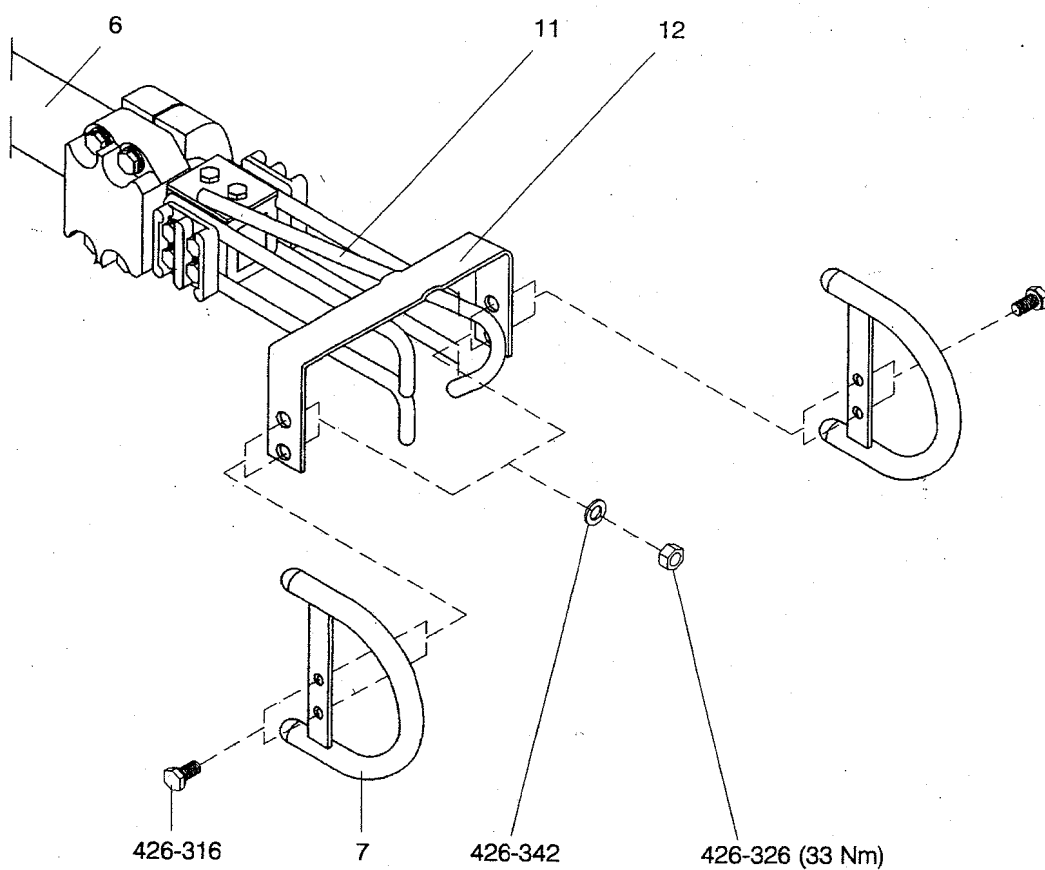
Установка разъединителя. Установка устройств защиты от короны (7) на пальцевой стороне (только для номинального напряжения 245...300 кВ)
